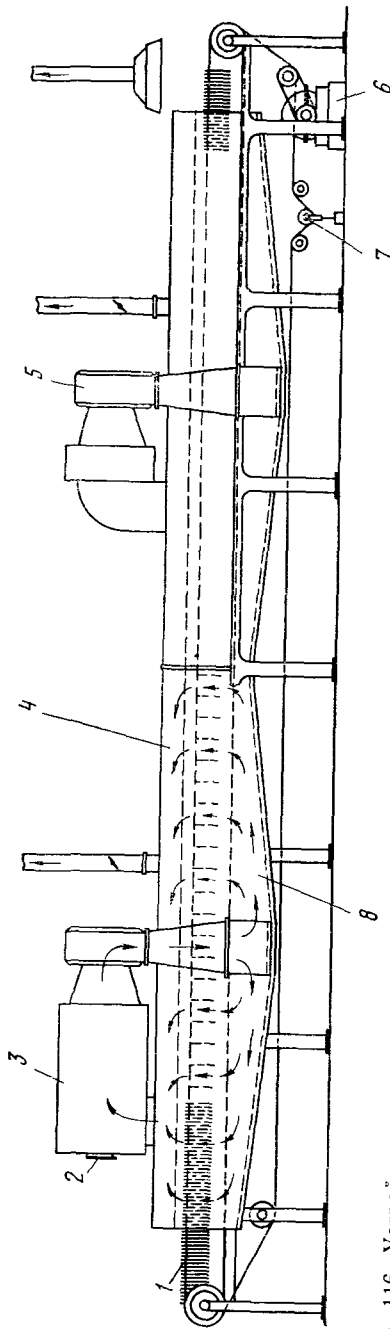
Устройство туннельного конвейерного сушила с распределительными каналами переменного овального сечения: 1 — цепь конвейера с пластинами, 2 — заслонка, 3 — калорифер, 4 — верхний сборный воздушный канал, 5 — рециркуляционный вентилятор, 6 — редуктор привода, 7 — натяжное приспособление, 8 — нижний распределительный воздушный канал
